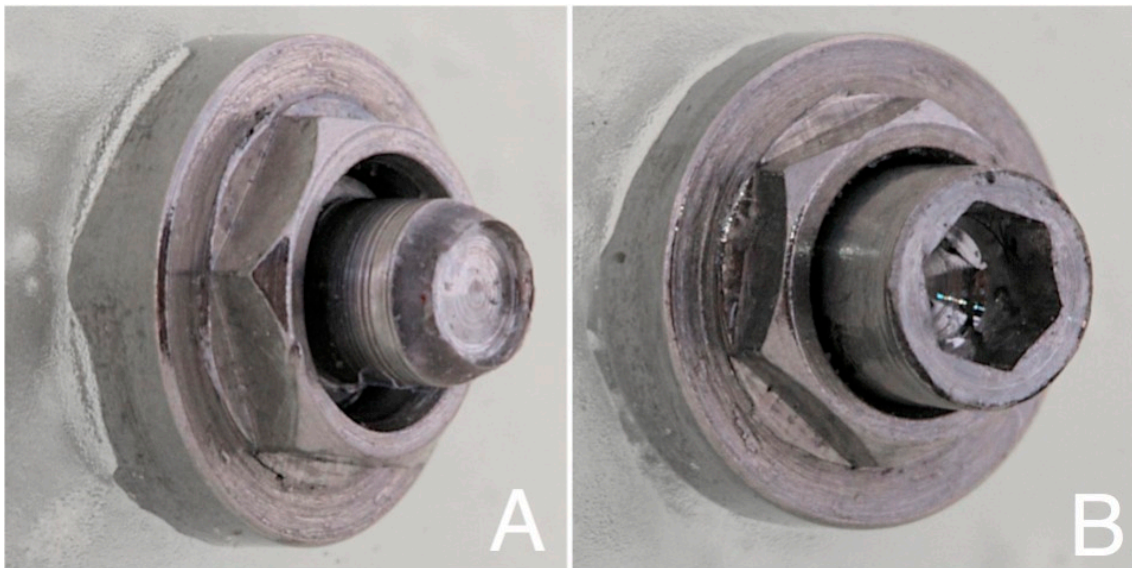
A: Tornillo control fracturado. B: Tornillo prototipo 3 fracturado.
